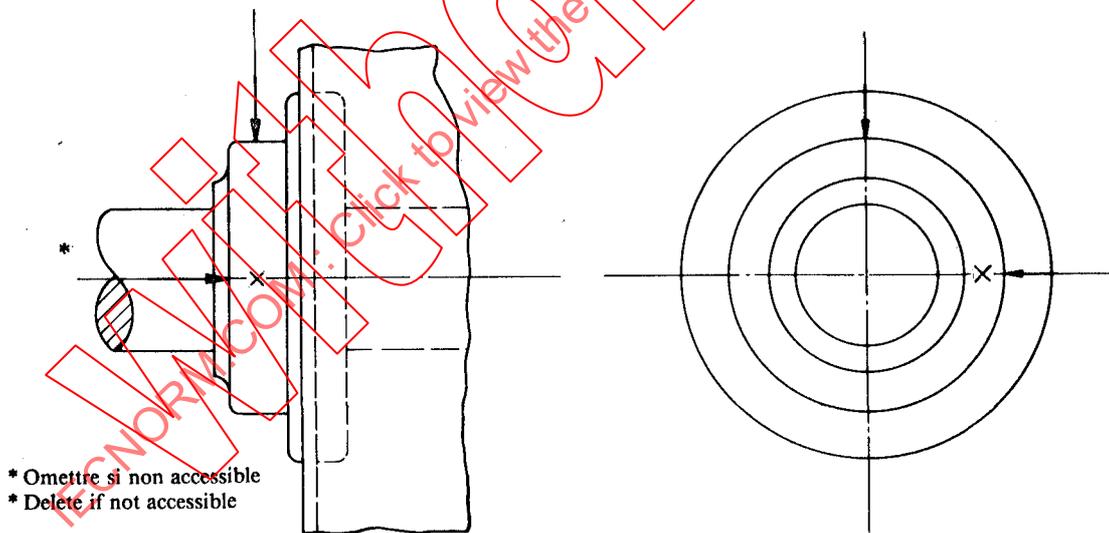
Emplacement des points de mesure pour des machines de hauteur d'axe supérieure à 400 mm, applicable aux deux extrémités de la machine.
